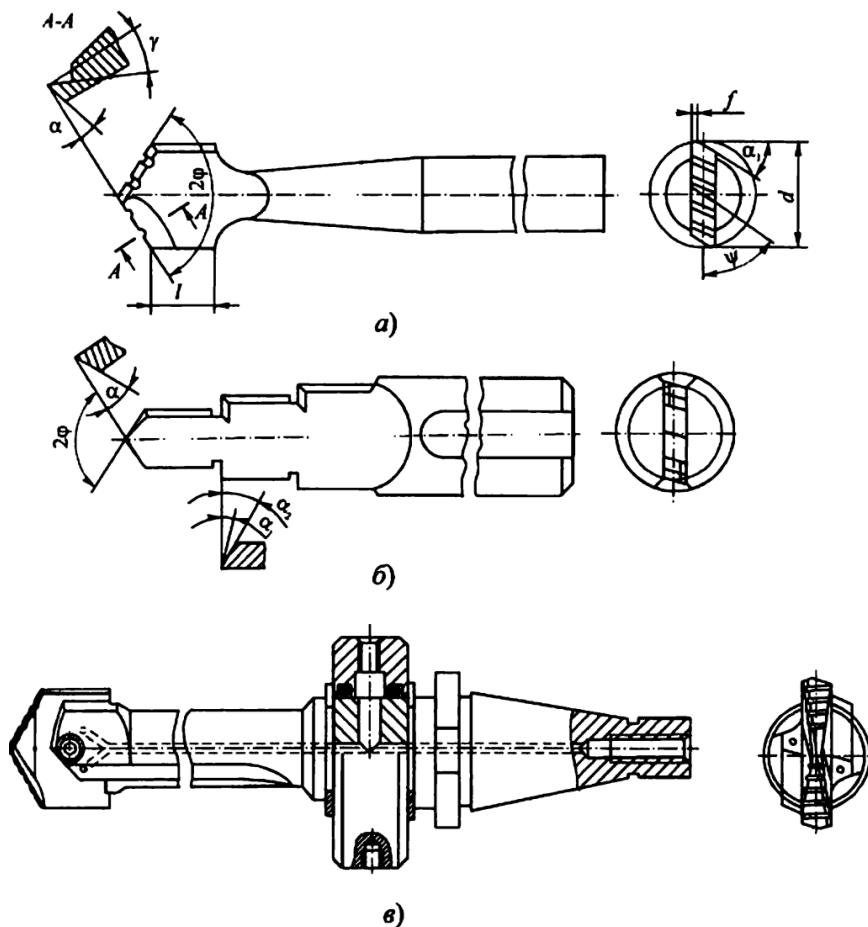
Перьевые сверла: а – цельное; б – для сверления ступенчатых отверстий; в – сборное, с внутренним напорным охлаждением
